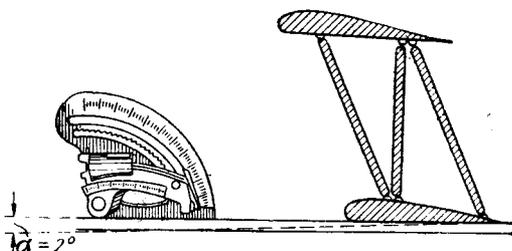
Проверка регулировки установочных углов крыльев с помощью угломера (размеры угломера увеличены).
